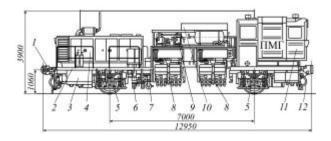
Путевой моторный гайковерт ПМГ: 1 – автосцепки; 2 – рама; 3 – топливный бак; 4 – дизель-электрический агрегат мощно-стью 200 кВт; 5 – колесные пары с колесномоторными блоками; 6 – тросовые пассивные рельсовые щетки; 7 – поролоновые ролики для смазки скреплений; 8 – блоки гайковертов; 9 – насосные станции; 10 – шкаф с электрооборудованием; 11 – кабина управления; 12 – тормозная система
